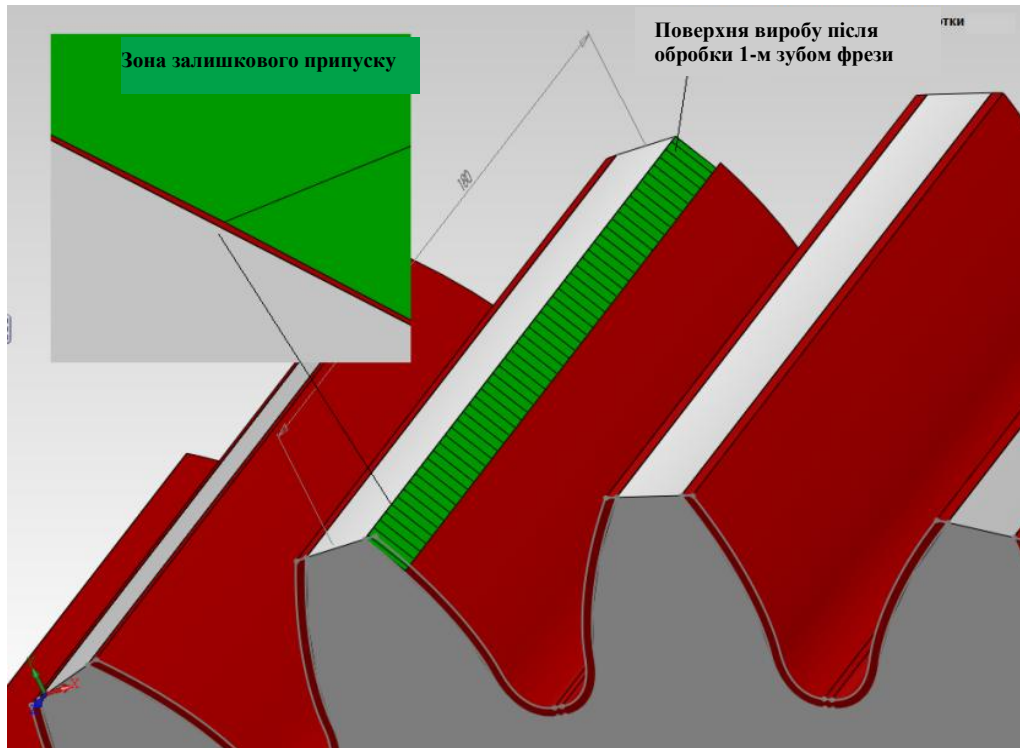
Формоутворення поверхневого шару одним зубом зубообробної фрези відновлених крупногабаритних зубчастих коліс
